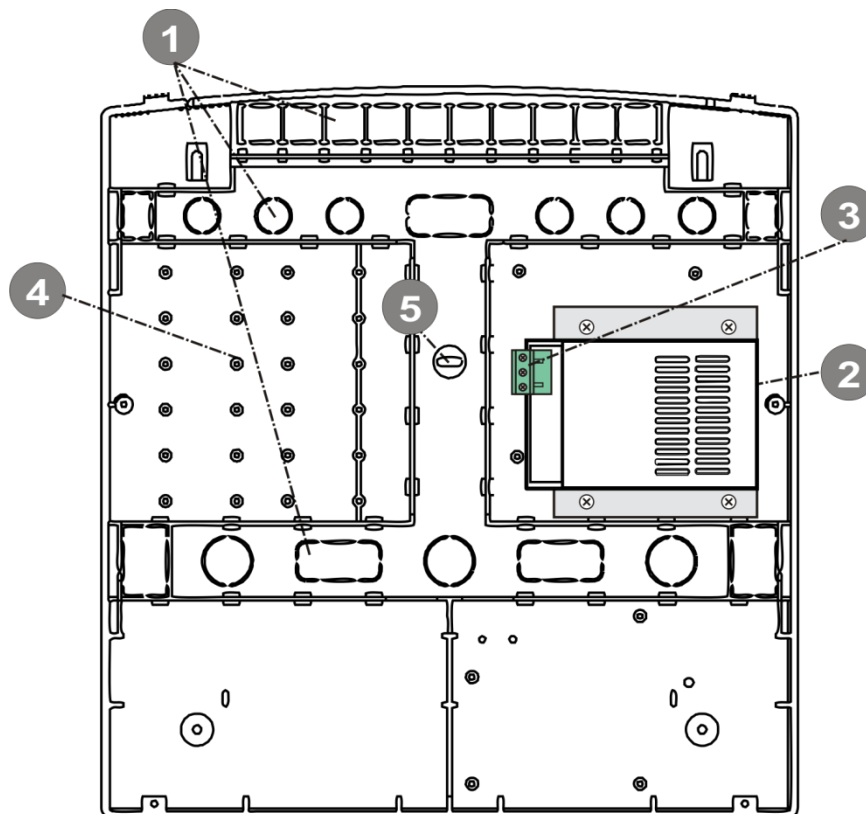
Внешний вид корпуса без основного модуля ППКП:
